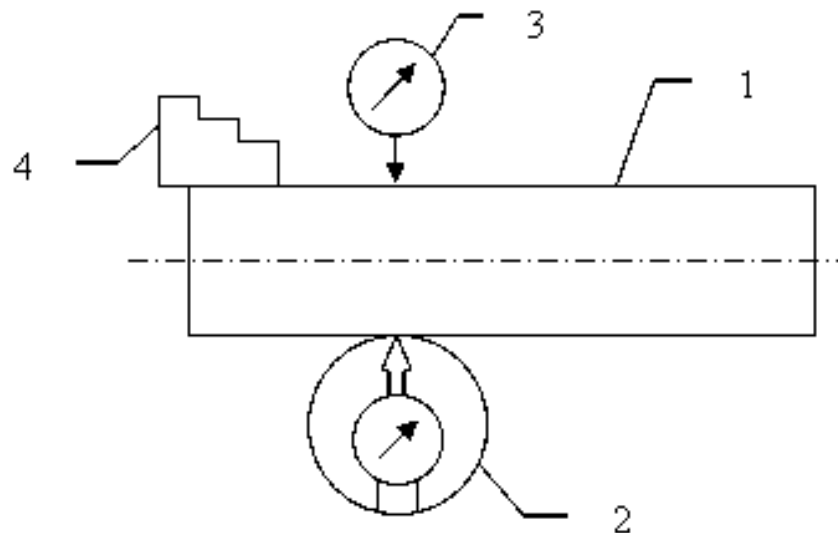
Схема лабораторной установки: 1 – заготовка, 2 – кольцевой динамометр, 3 – индикатор часового типа, 4 – патрон.
